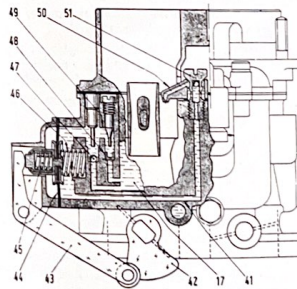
Carburador Bressel-Weber 30 DIC 1.
